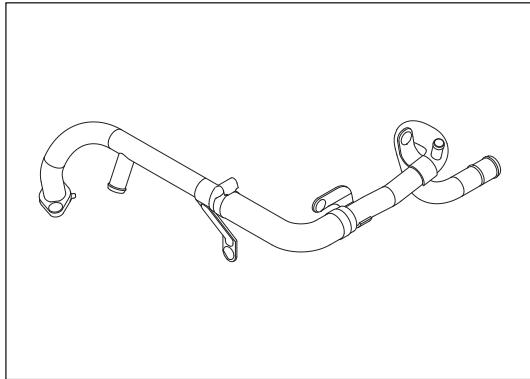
Проверка отводящей трубы нагретой ОЖ
